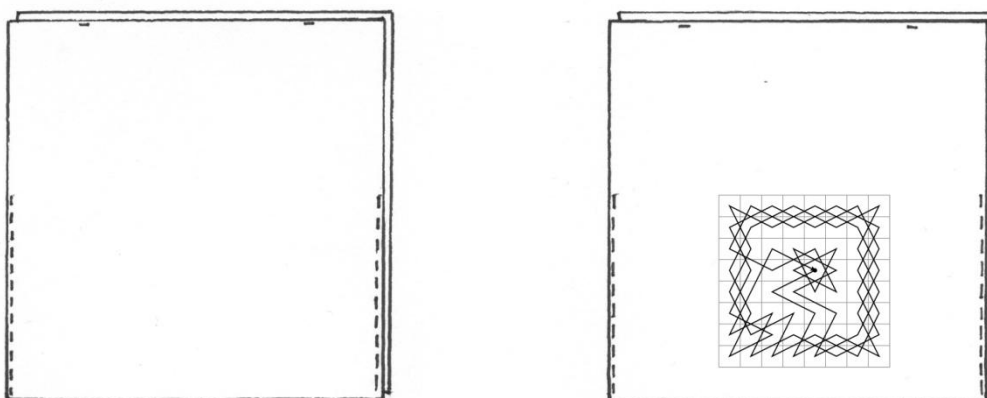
Technický náčrt předního a zadního dílu bolerka.
